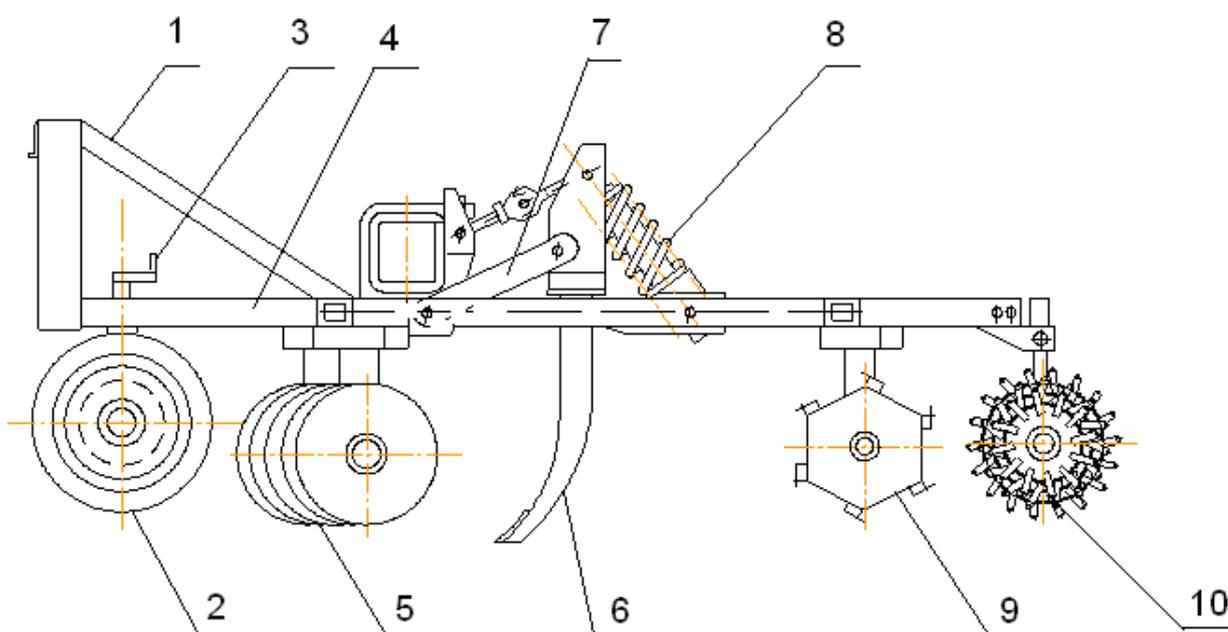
Агрегат для противозерозионной обработки почвы
